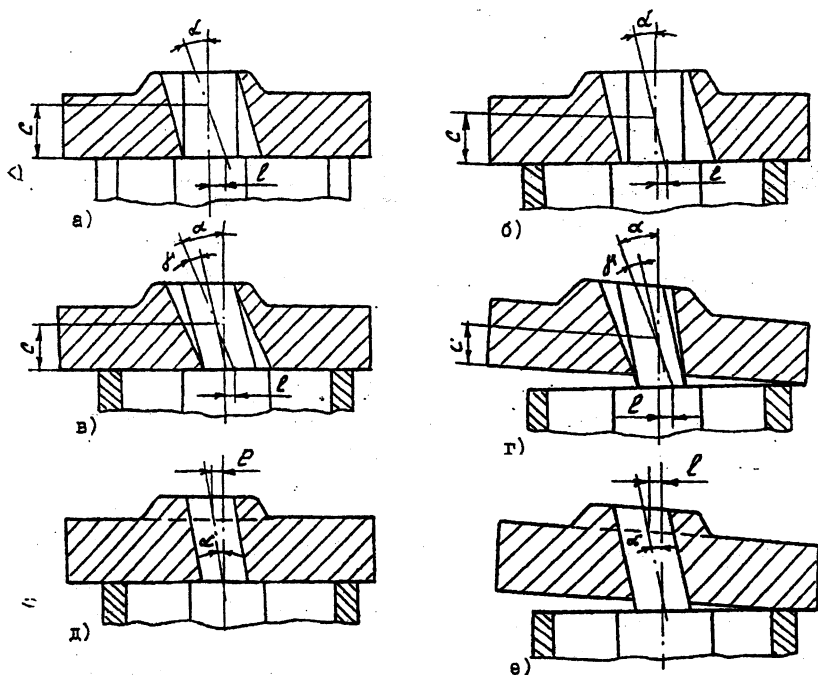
Возможные варианты взаимного положения детали и установочных элементов приспособления при зубофрезеровании
